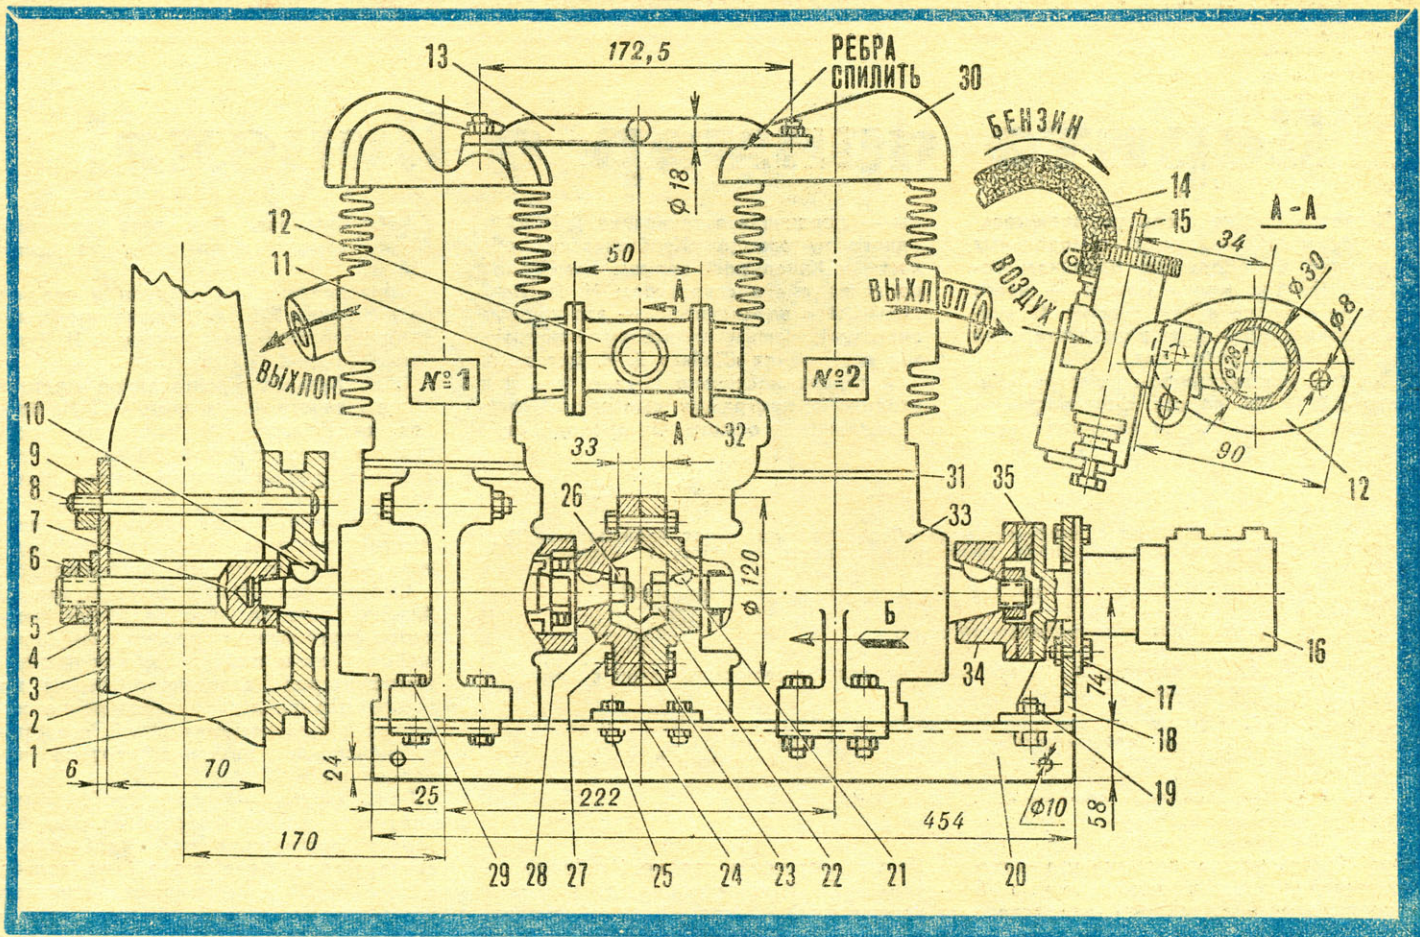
Схема соединения и детали спарки двигателей ПД-10 для установки на аэросани:
